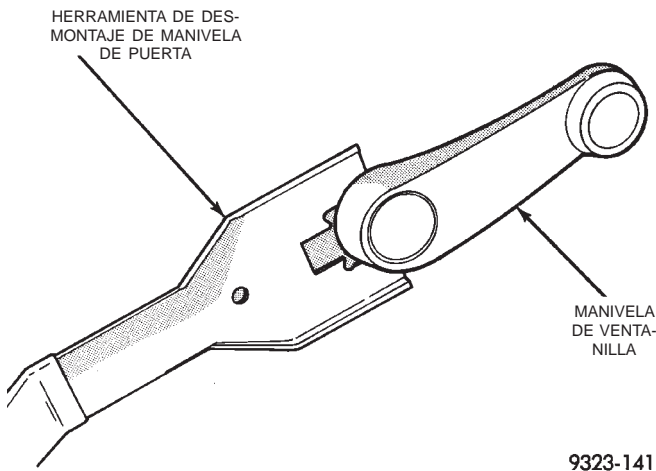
Desmontaje de la manivela reguladora de ventanilla - Característico
